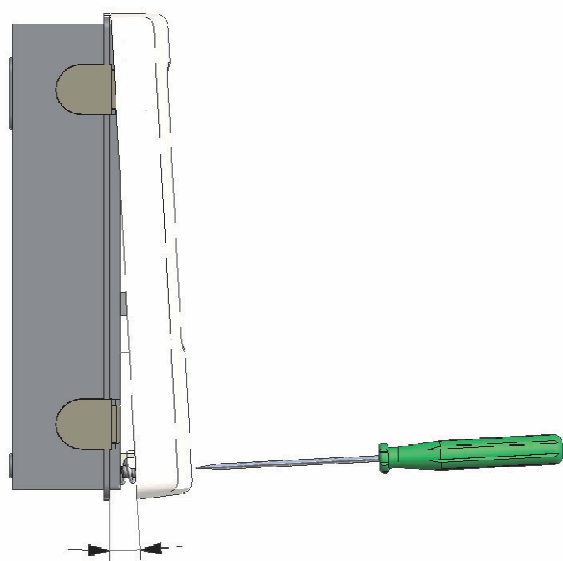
Крепежная крышка Регулятора SRS3
